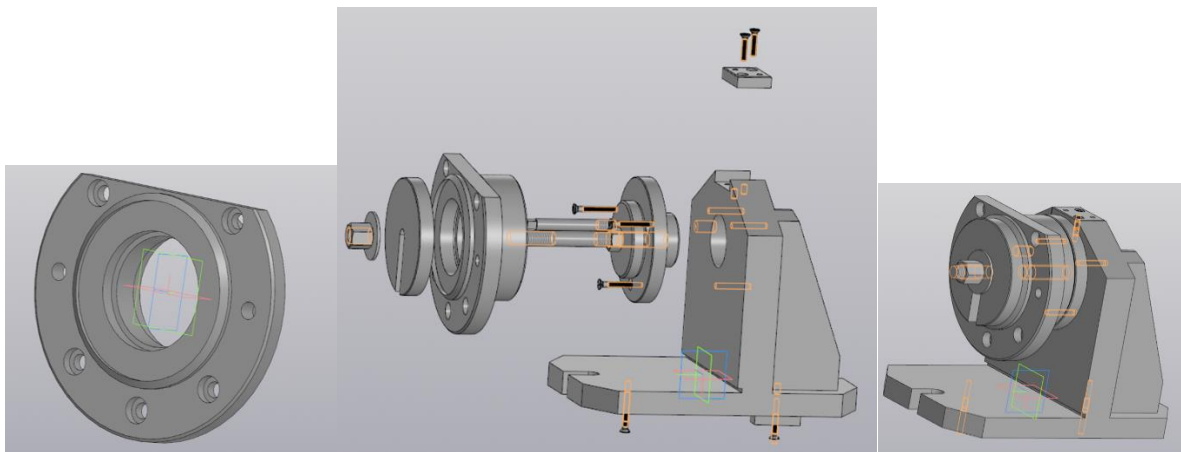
3D-модели детали “Втулка” (слева) и фрезерного приспособления (справа)
